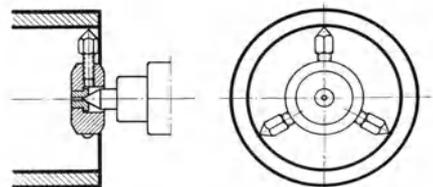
Gewöhnliche Aufnahme von Hohlzylindern auf Zentrierstern.
